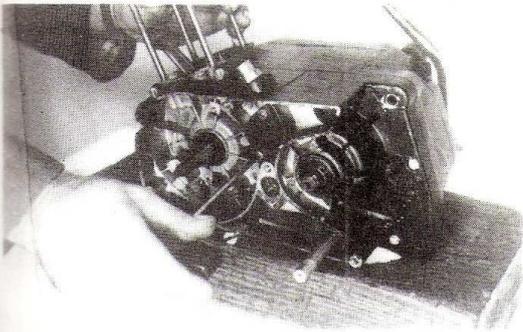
Desmontar capuchón tambor selector y la junta capuchón seguro tambor.
